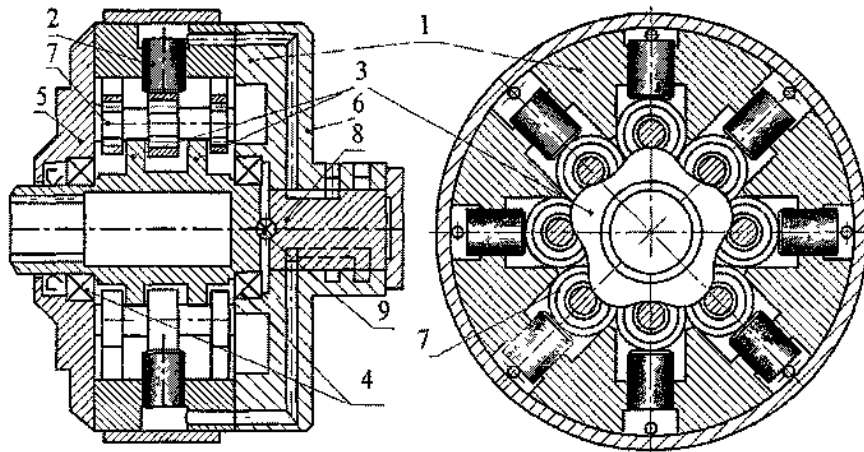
Радиальнопоршневой гидромотор конструкции ВНИИГидропривода с цилиндрическими траверсами 7, обеспечивающими разгрузку поршней 2 с помощью пар качения
